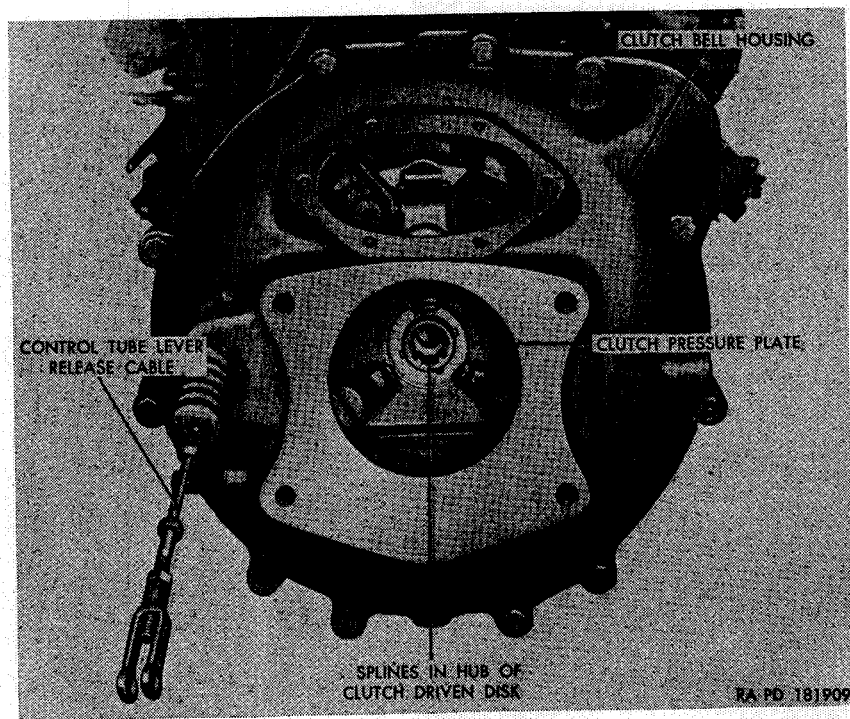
Carter d'embrayage depuis l'arrière, transmission déposée
